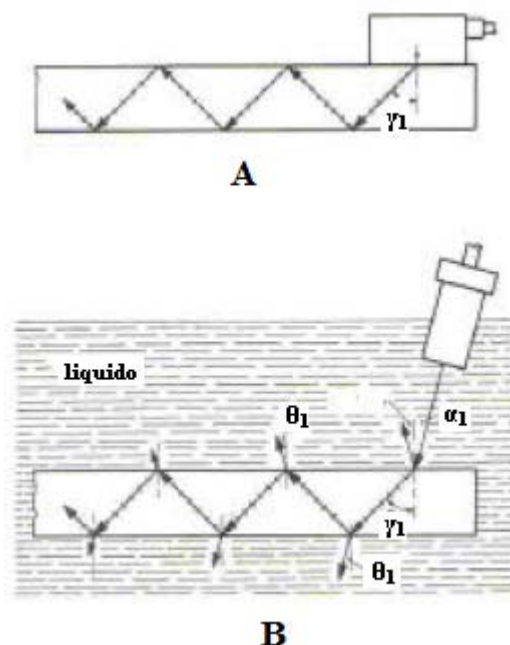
a) Técnica de contacto; b) Técnica de inmersión.
